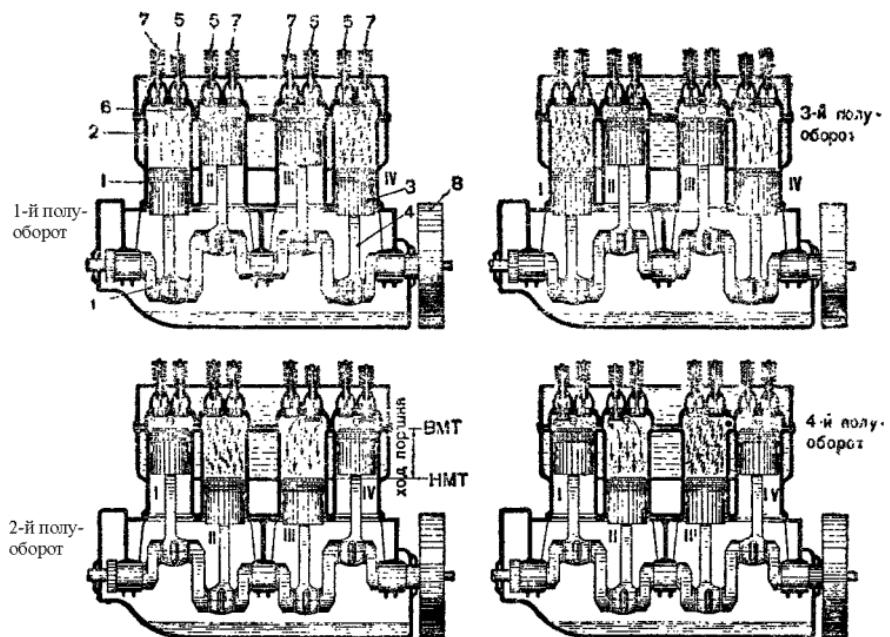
Схема работы четырёхцилиндрового двигателя.
